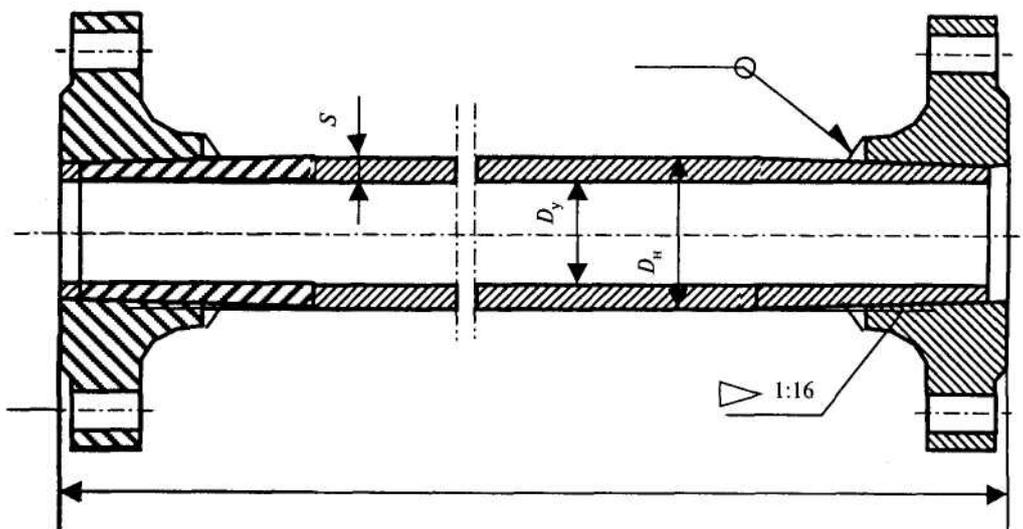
Схема трубы с приваренными фланцами (тип Б)
